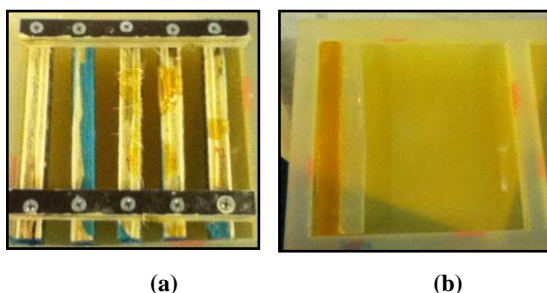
(a) Molde de madeira desmontável, revestido de filme desmoldante, (b) Molde de silicone
